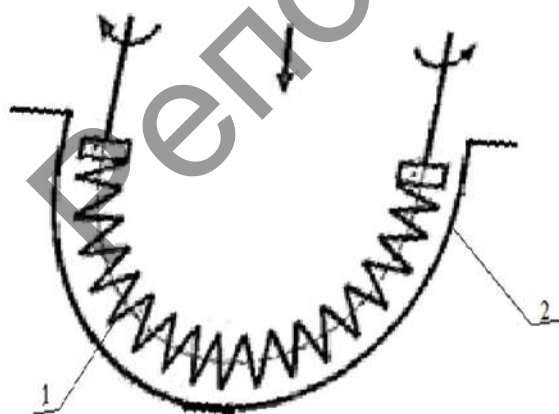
Кинематическая схема рабочего органа и камеры обработки
